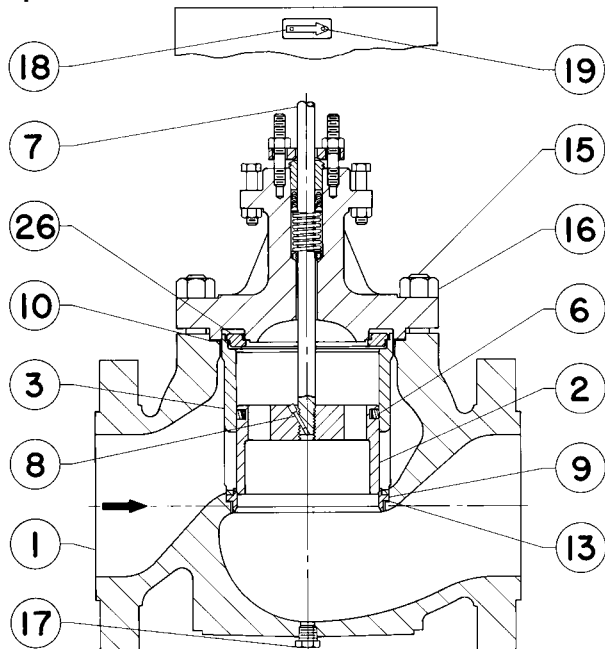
Клетка Whisper Trim III с дополнительной сливной заглушкой
